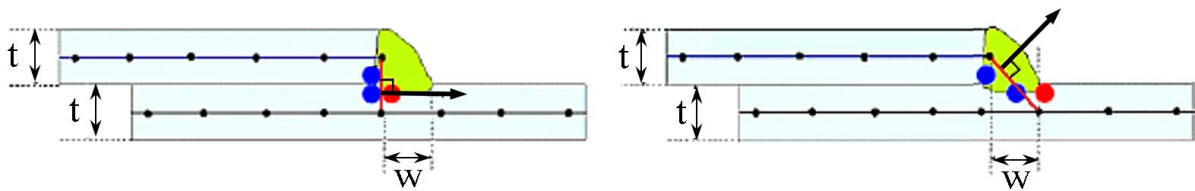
Esboço de modelamento de união soldada por superfície média.
